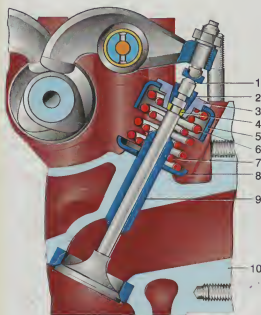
Клапанный механизм двигателя 331.10. 1 – стержень клапана; 2 – сухарь; 3 – упор; 4 – уплотнительное кольцо; 5 – колпак; 6 – наружная пружина; 7 – внутренняя пружина; 8 – чашка; 9 – направляющая втулка; 10 – головка цилиндра.
